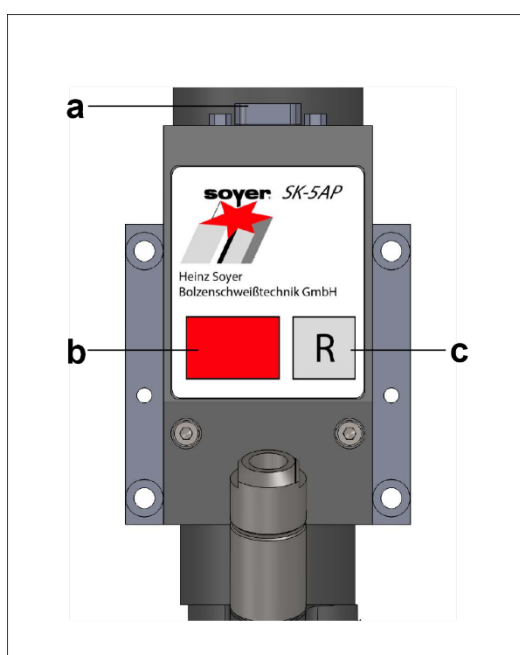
Bolzenschweißkopf SK-5AP
